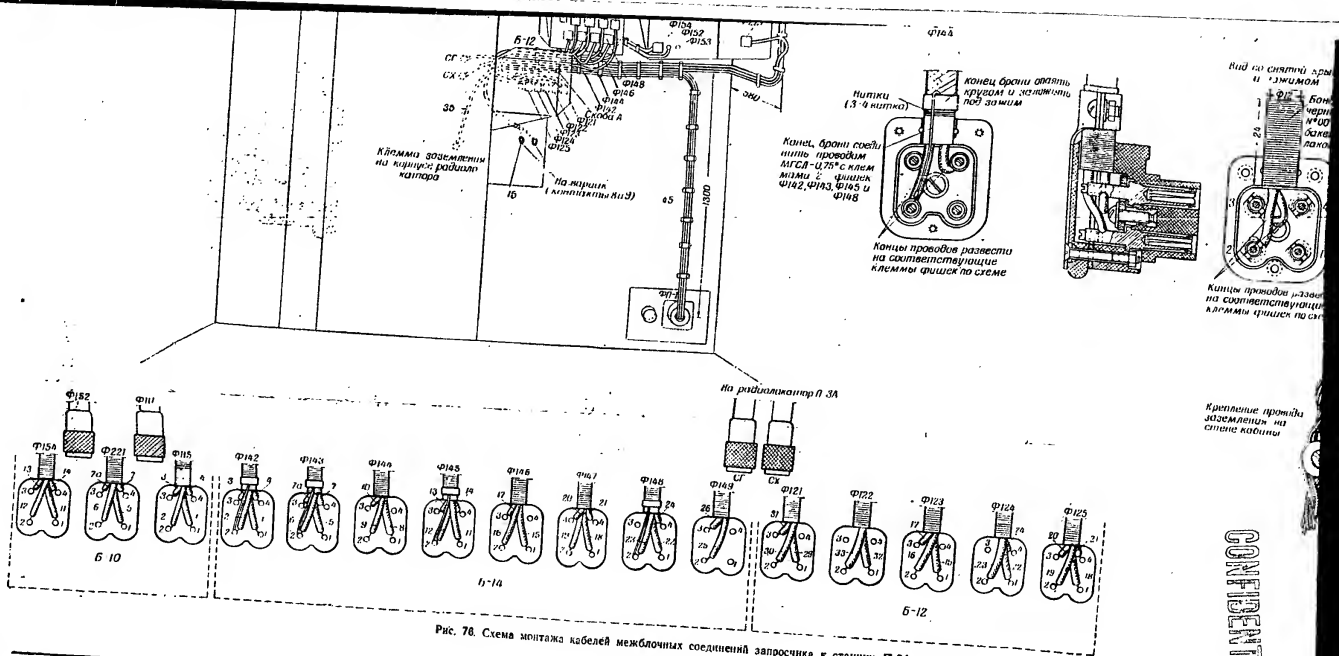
Схема монтажа кабелей межблочных соединений радиоприемника к станции Р-3А
